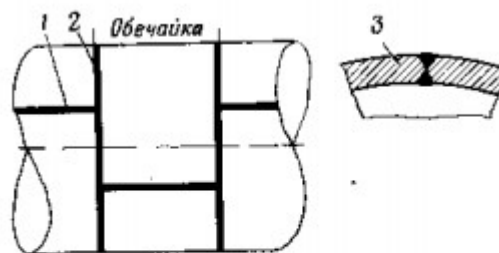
Узел сварной обшивки прочного корпуса ПЛ:
